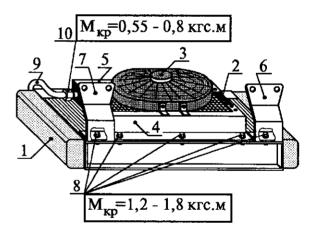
Установка агрегатов и узлов климатической установки на радиатор охлаждения автомобиля ГАЗ-3102:
